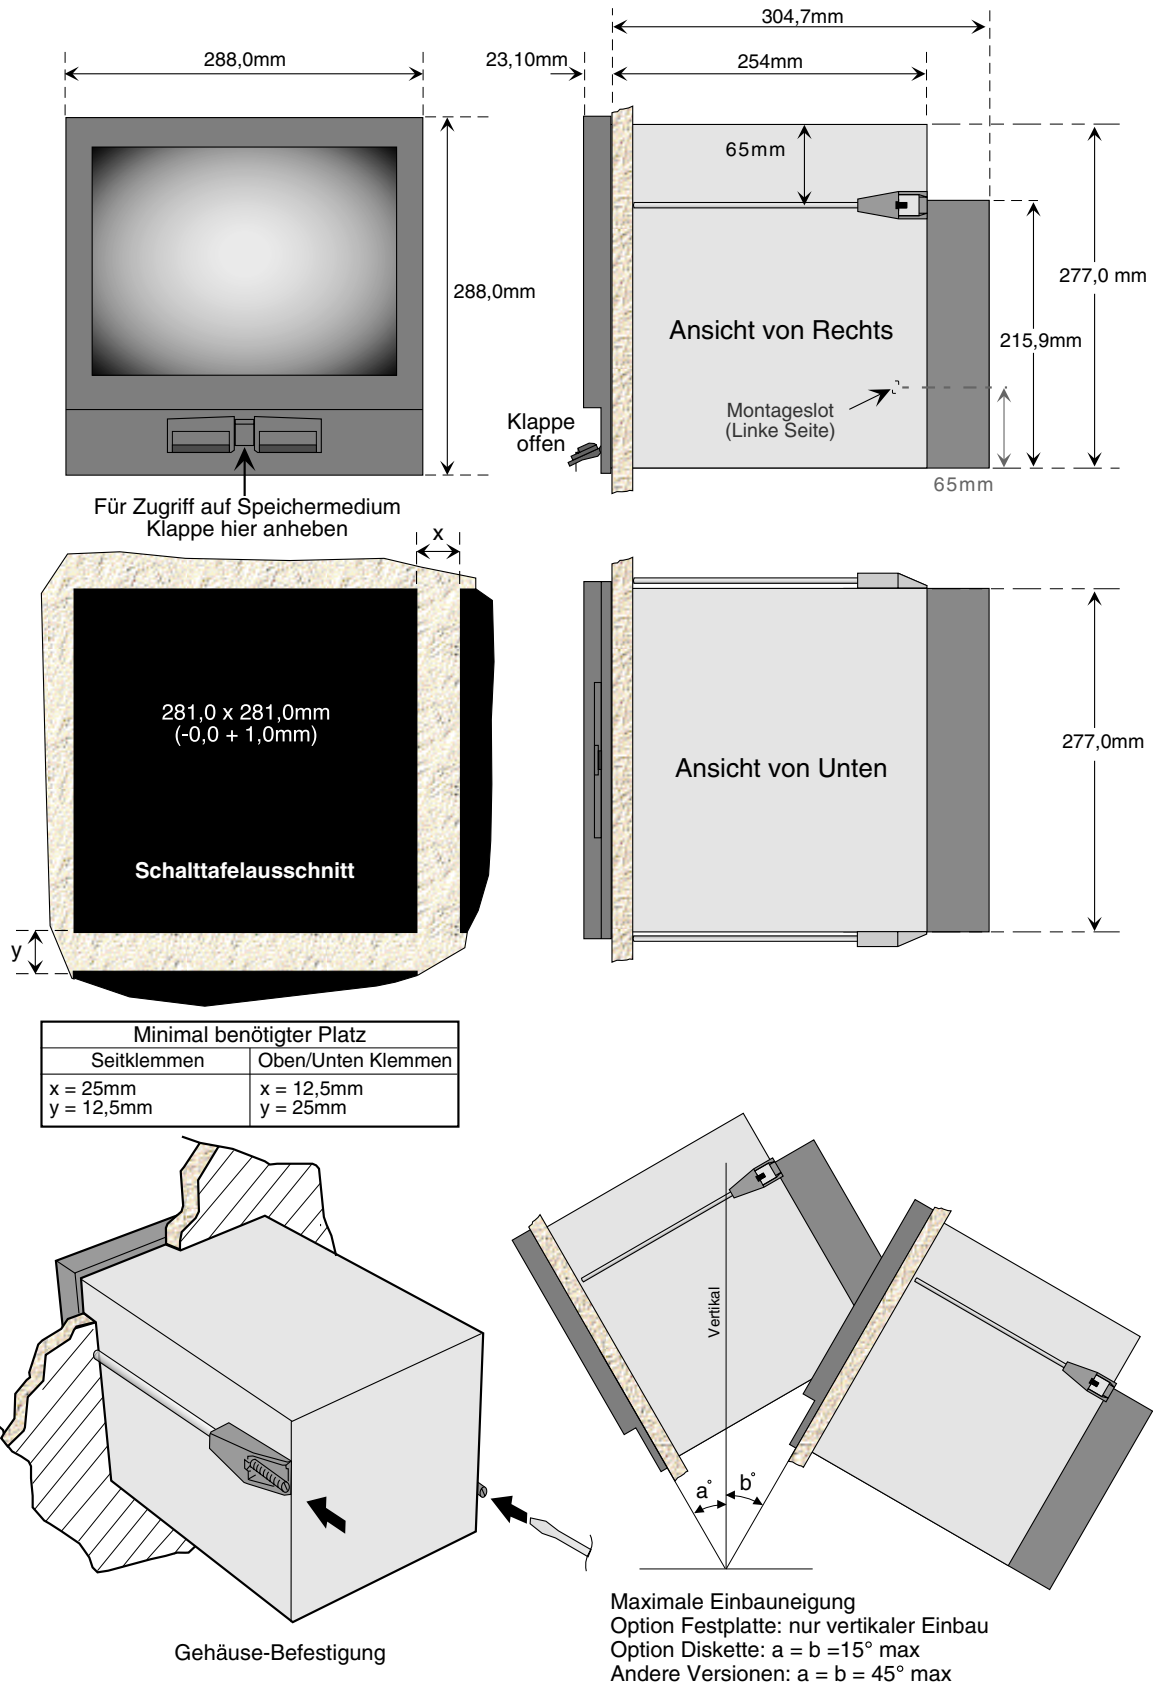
Mechanische Installation - Schreiber im 277x277mm Gehäuse
